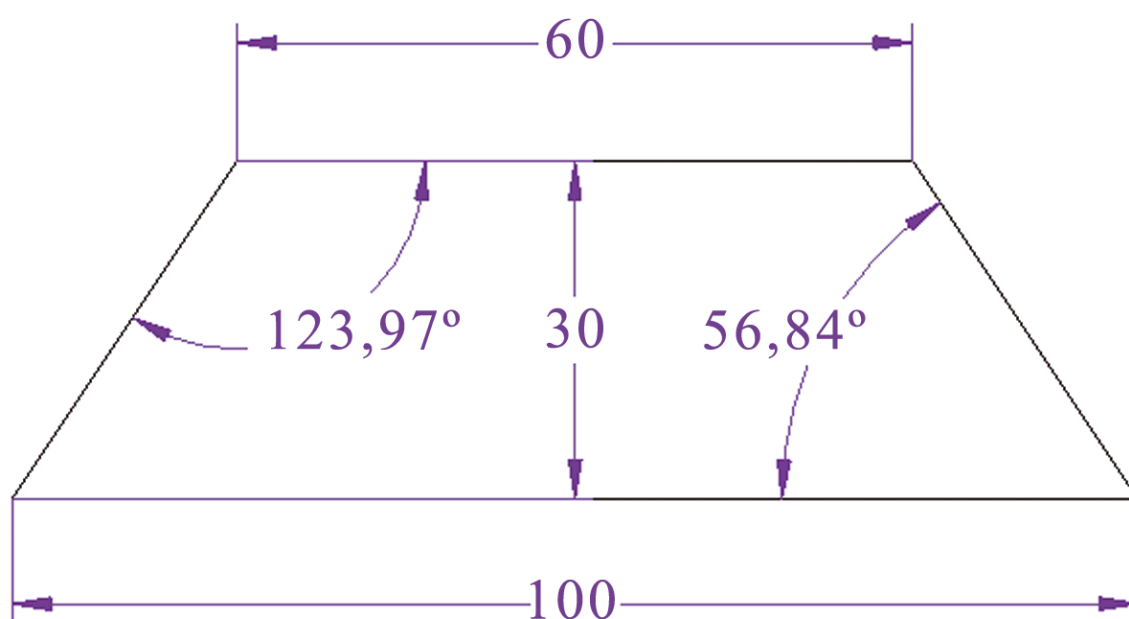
Dimensiones y ángulos de la sección del molde.
